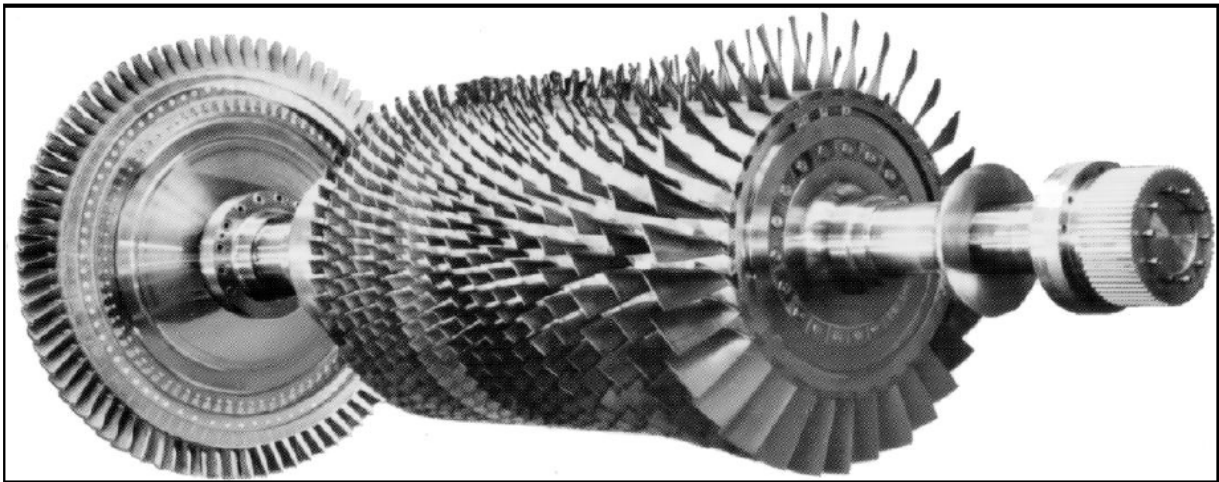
Vue de l'ensemble rotor turbine H.P. du compresseur
